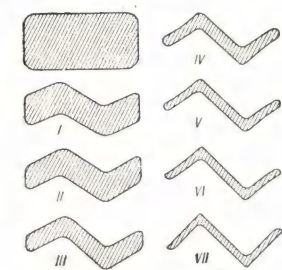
Схема последовательного изменения сечения (калибровки) при прокатке зетобразного профиля.
